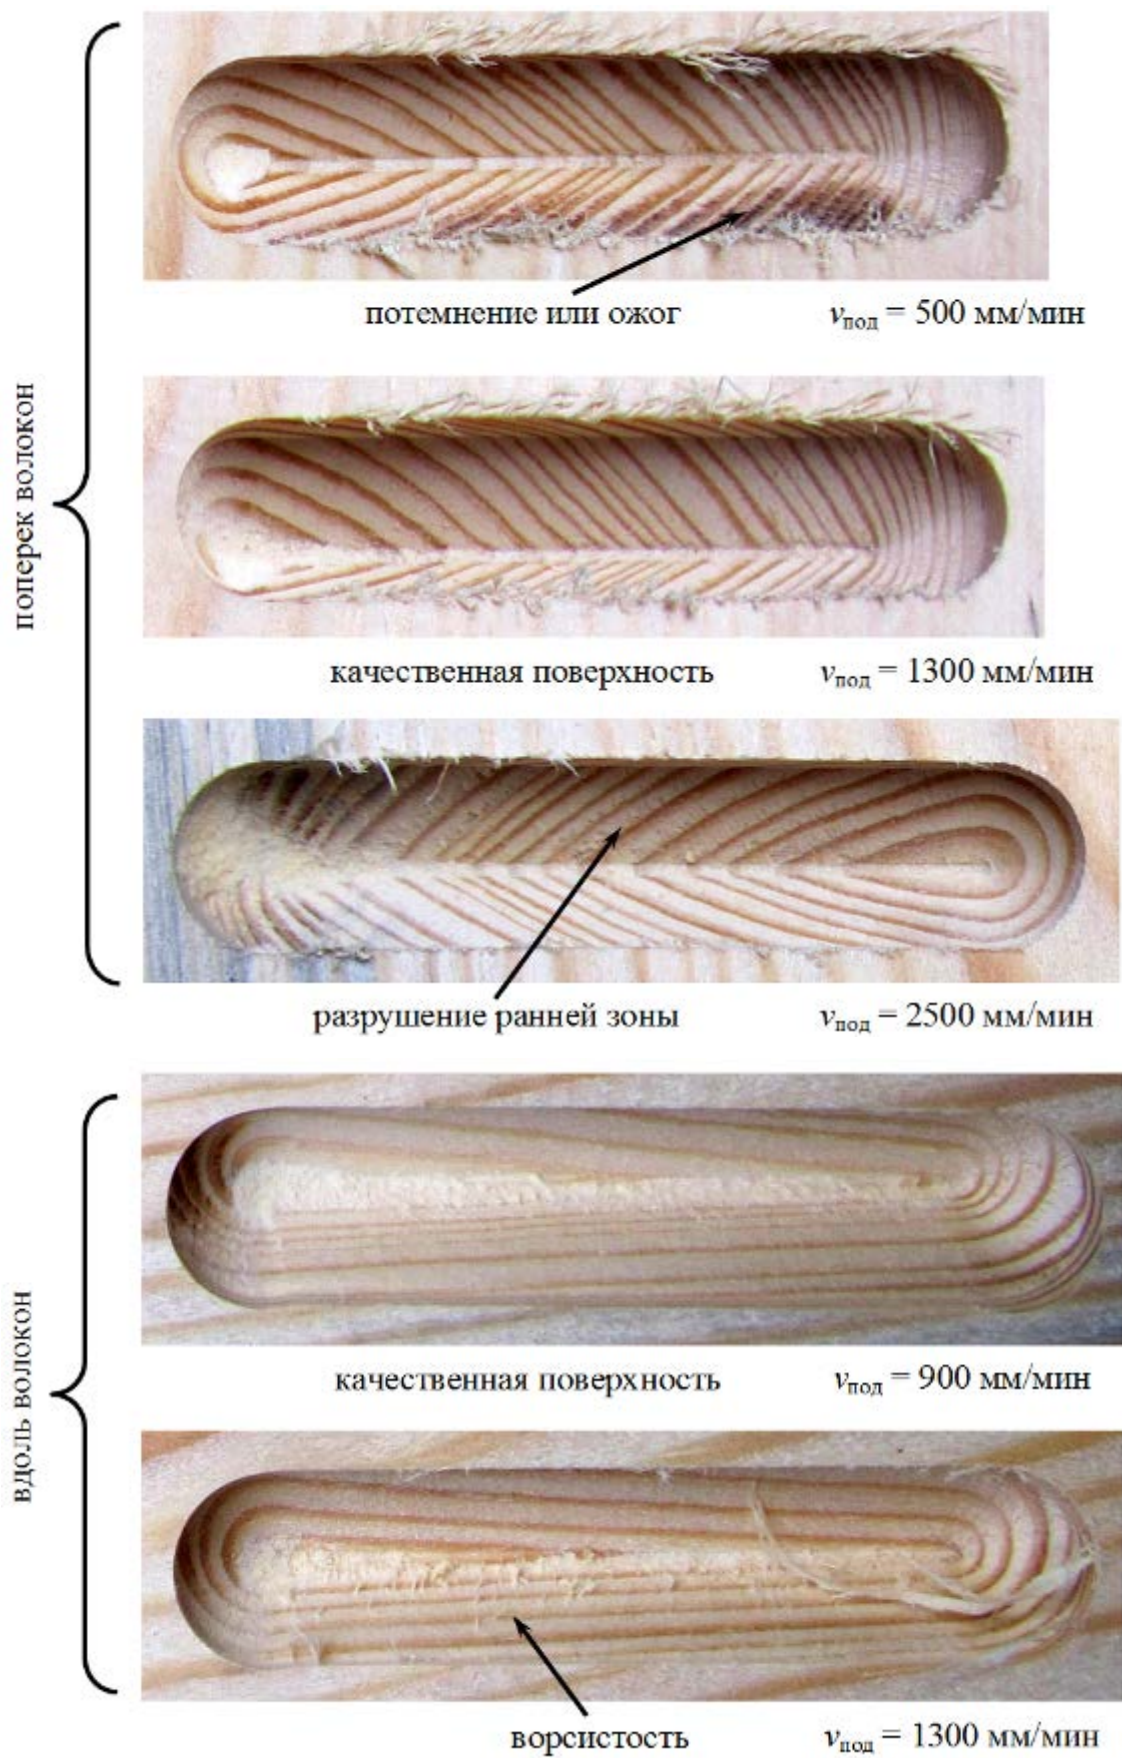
Качественно обработанная поверхность и дефекты фрезерования древесины сосны поперек и вдоль волокон
